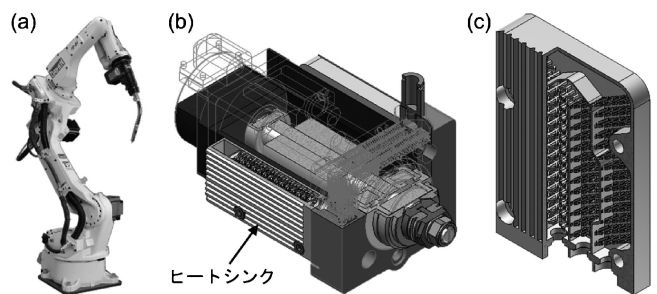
シンクロフィード溶接システム：(a) アーク溶接ロボットの外観写真, (b) ワイヤ送給装置, (c) ヒートシンクの CAD カットモデル。(株)ダイヘン提供)
